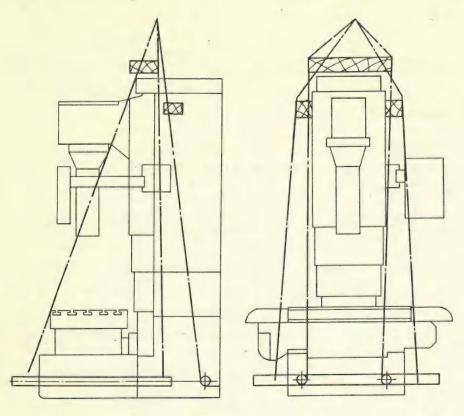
Схема транспортирования станка 2733[[ Масса станка 3500 кг
